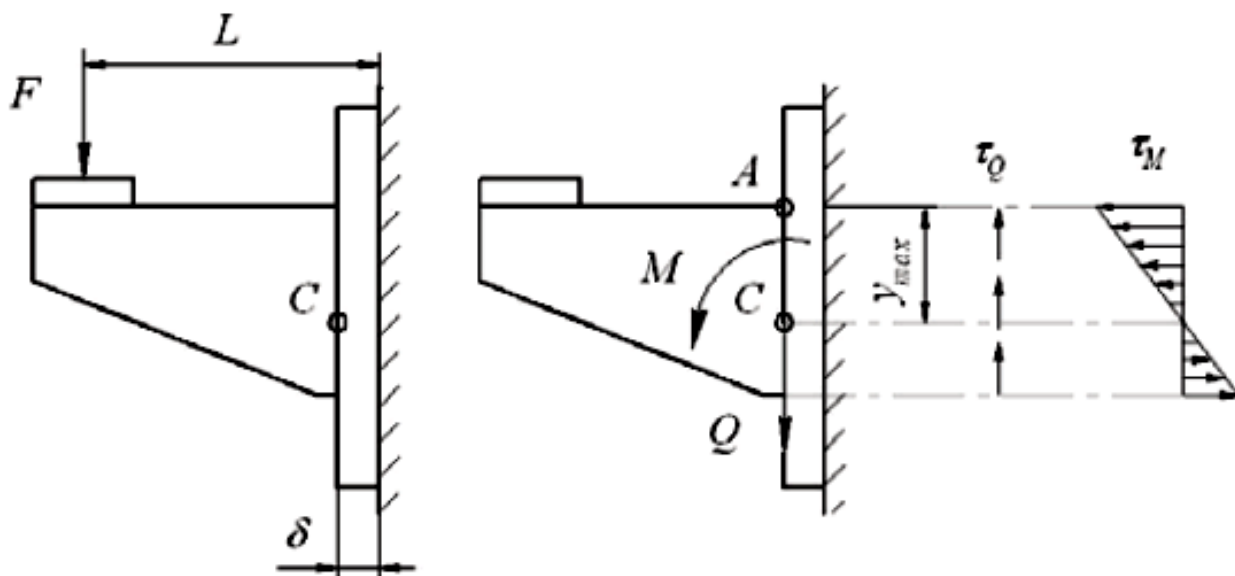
Расчетная схема определения усилий, действующих на сварное соединение кронштейна
